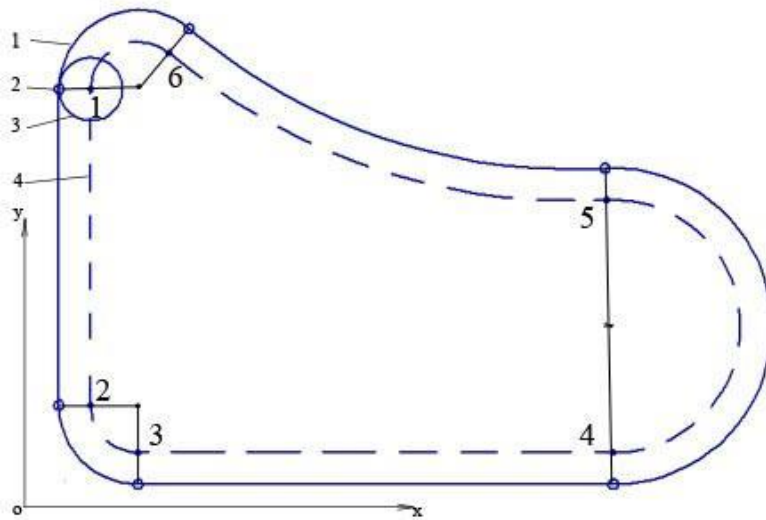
Обработка контура на вертикально-фрезерном станке
